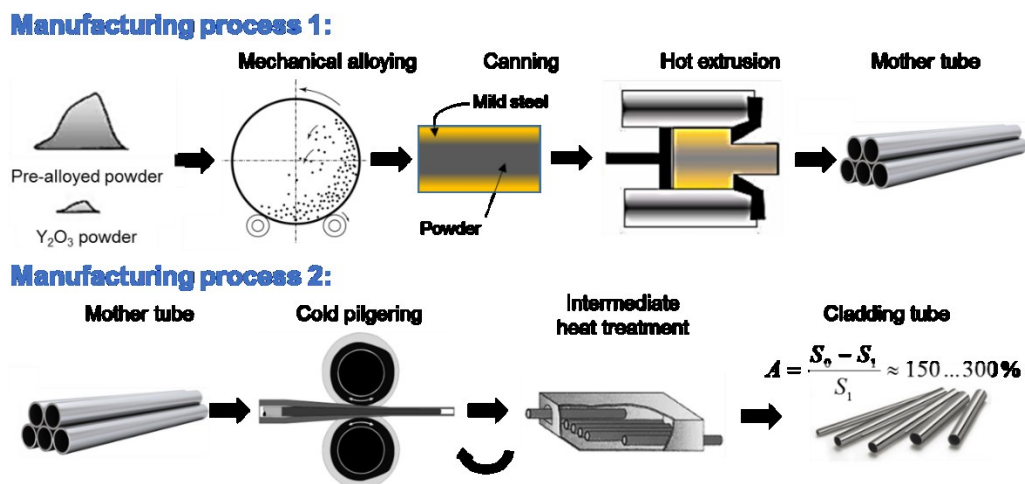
Chaîne de production de tubes en acier ODS par extrusion à chaud et laminage à froid, [Inoue et al, 2007]
